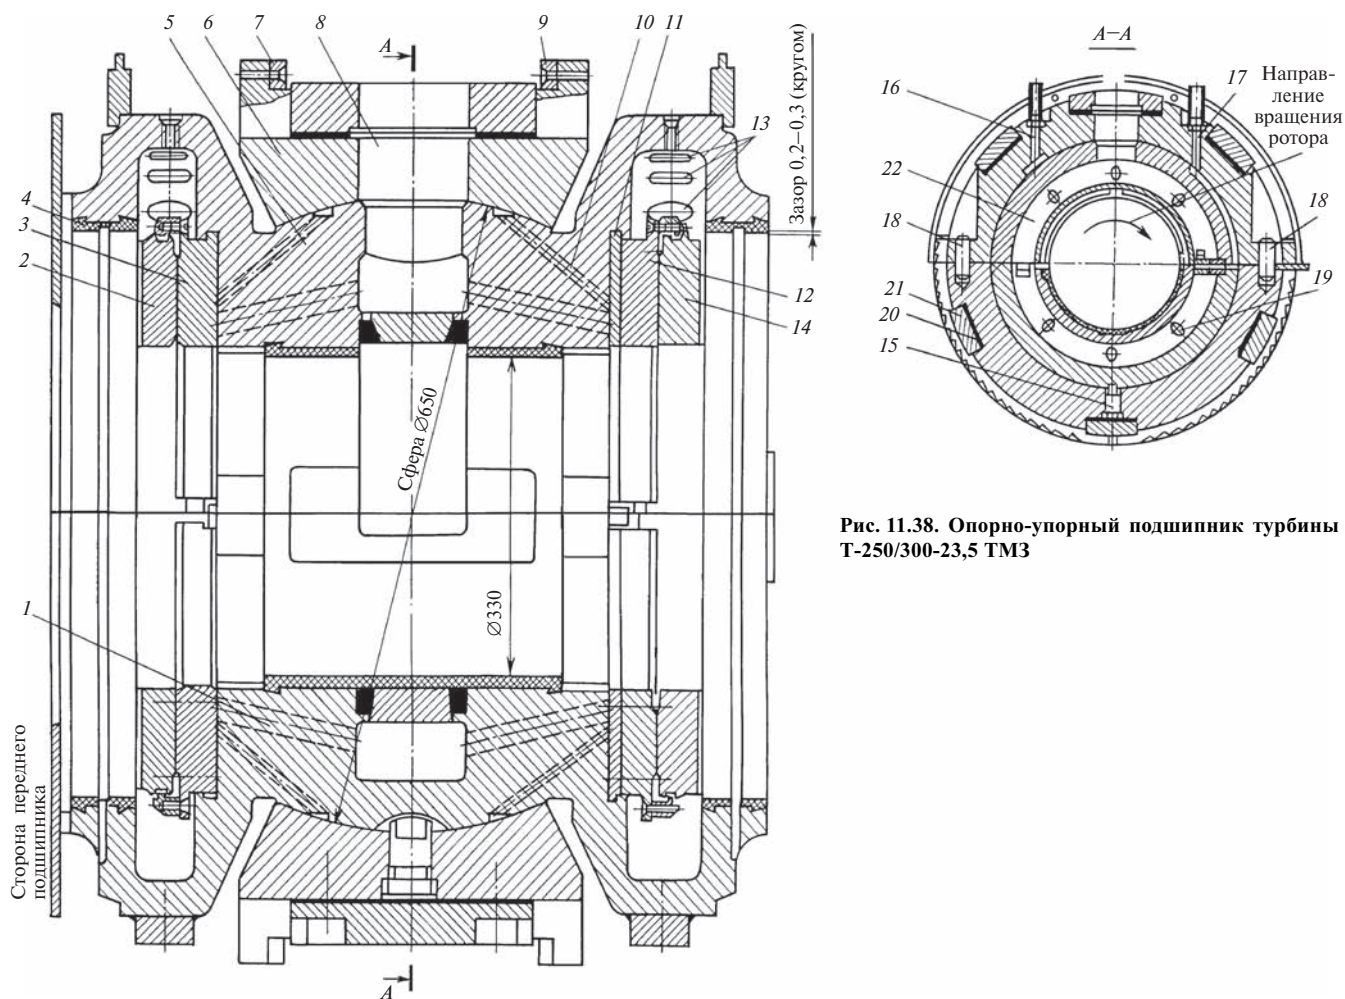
Опорно-упорный подшипник турбины Т-250/300-23,5 ТМЗ
